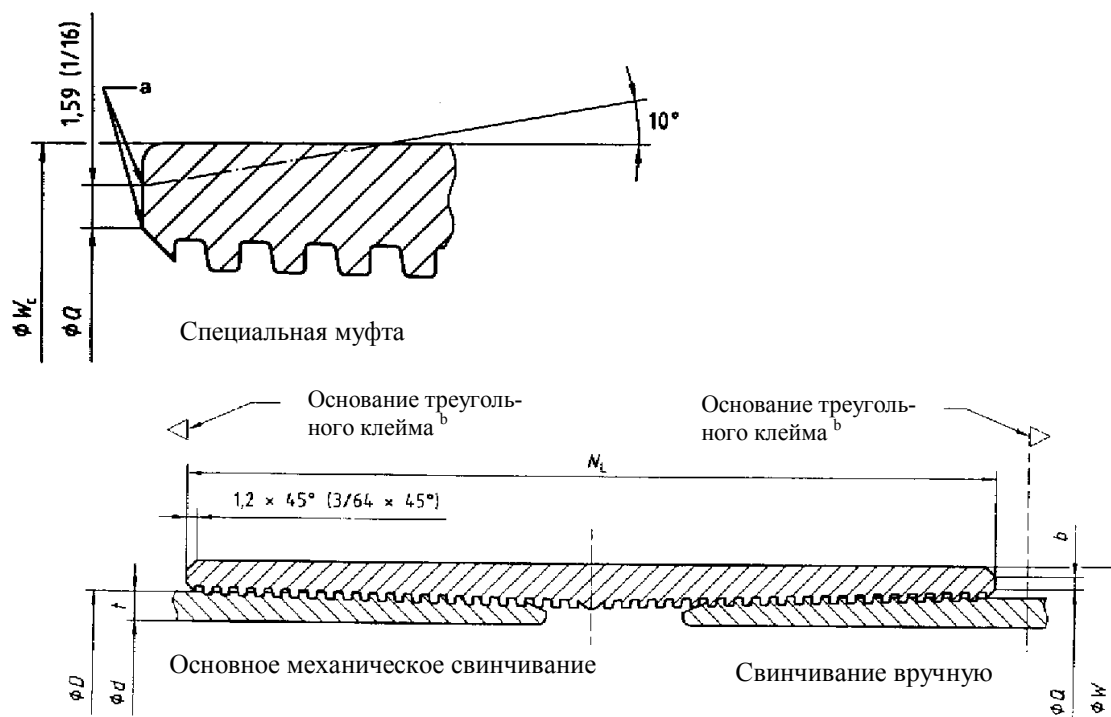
Обсадные трубы и муфта с короткой закругленной резьбой
